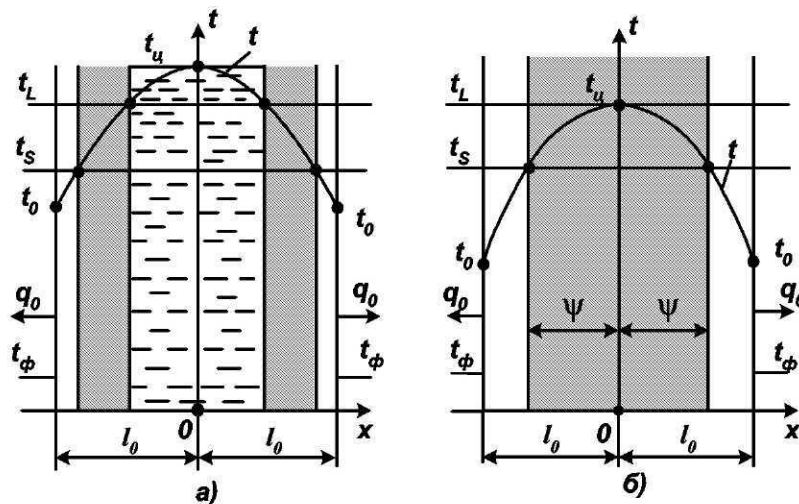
Схемы затвердевания элемента плоской отливки в металлической форме
